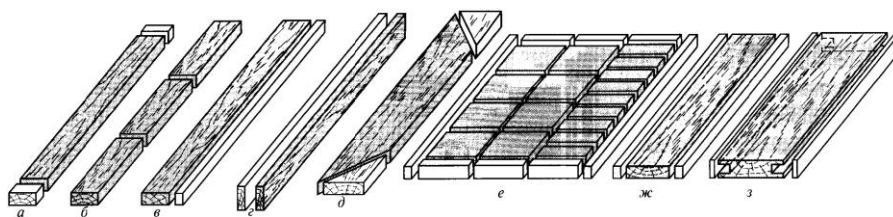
Види обробки на круглопилкових верстатах: *а* – торцювання заготовки; *б* – розкрій кратної заготовки по довжині; *в* – поздовжнє розпилювання по ширині; *г* – реброве розпилювання; *д* – розпилювання під кутом; *е* – розкрій плитних матеріалів; *ж* – обпилювання крайок щитів; *з* – обпилювання крайок і вибірка пазів
